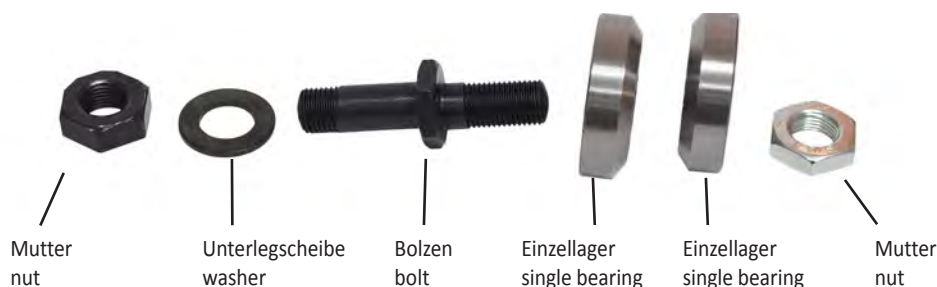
Montage von Einzellagern und Bolzen | Fig.3: Mounting of single bearings and bolts
